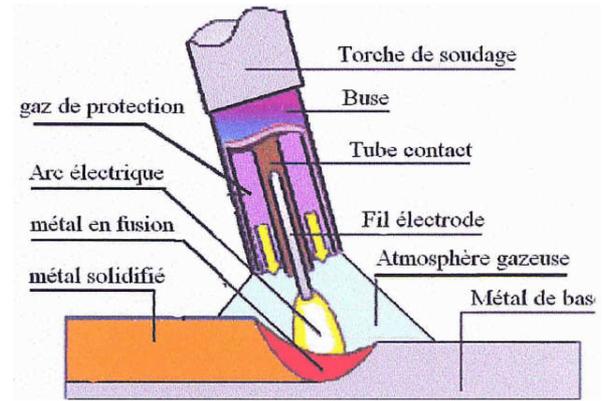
Soudage semi-automatique (MIG) [3].
